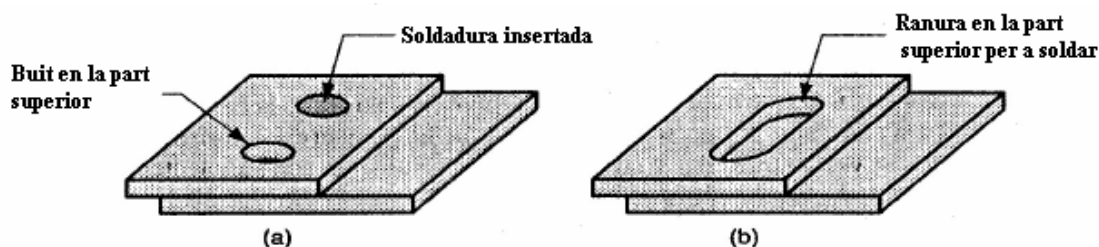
(a) Soldadura amb inserit i (b) soldadura en ranura.
